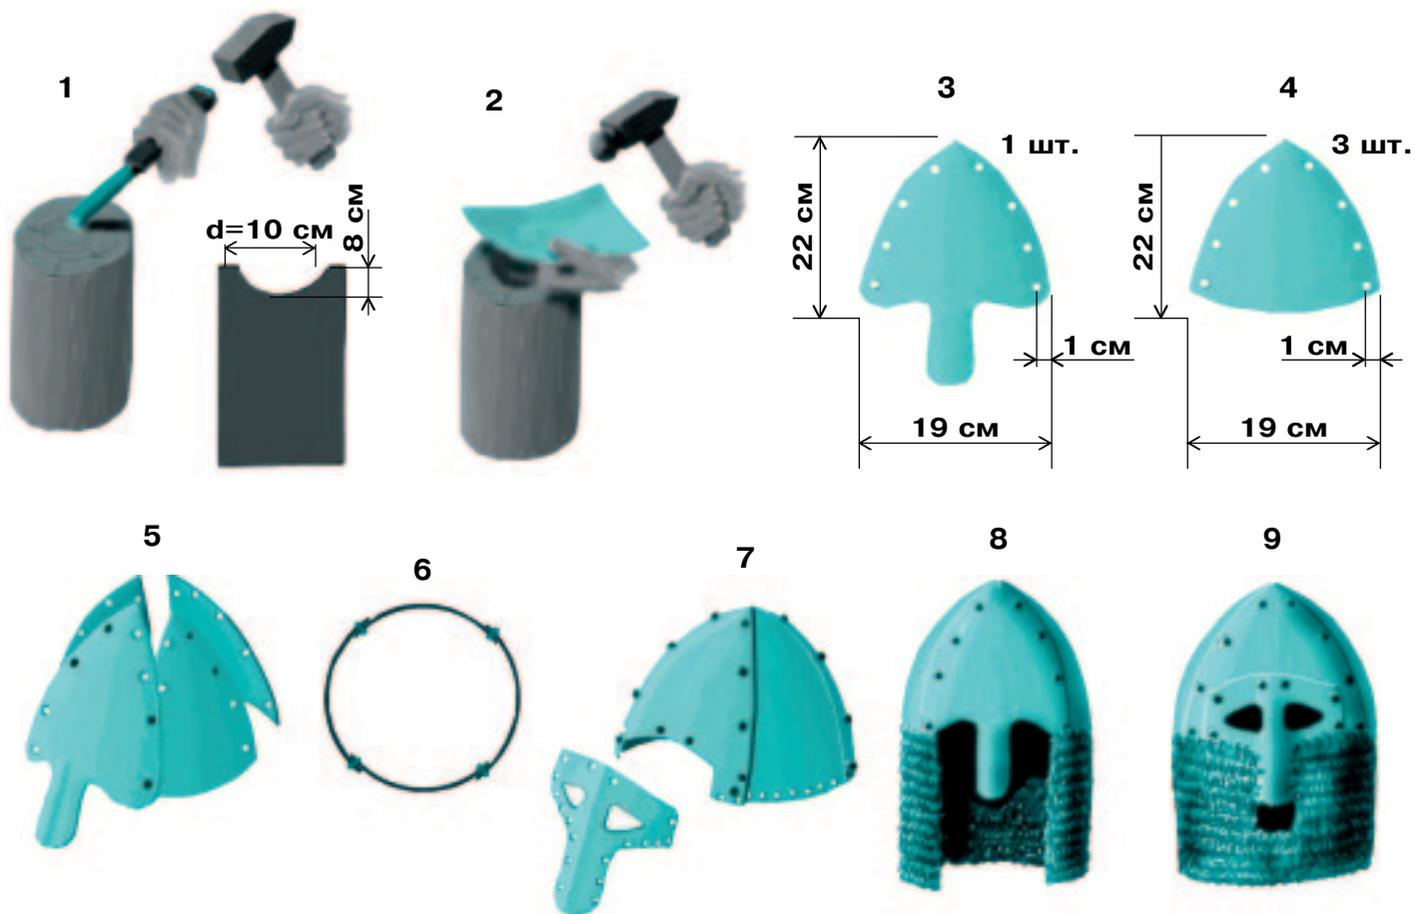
Этапы изготовления металлического шлема: 1 — изготовление и размеры формы для выколотки; 2 — процесс выколотки закругленным молотком; 3, 4 — элементы металлического шлема; 5 — готовые элементы шлема; 6 — положение скрепленных элементов; 7 — сборка шлема с «личной»; 8, 9 — готовые шлемы.
